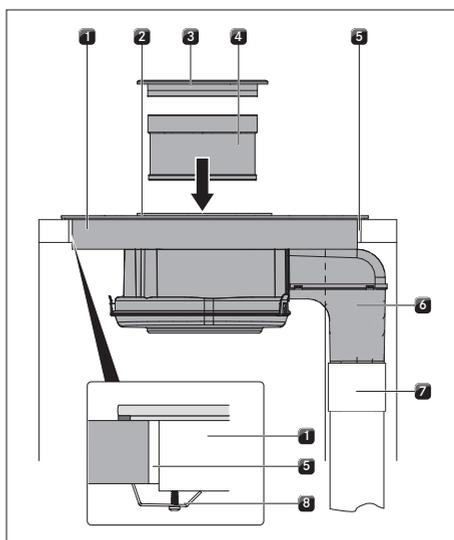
Chiudere il canale di scarico dell'aria + fissaggio
